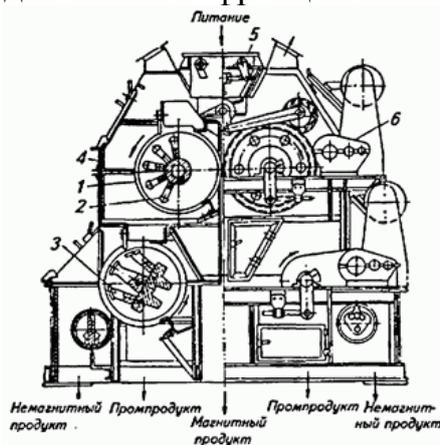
Магнитный барабанный сепаратор типа 4ПБС-63/200: 1 – барабаны; 2, 3 – пятиполюсные и трехполюсные магнитные системы; 4 – рама с кожухом; 5 – приемная коробка с распределителем питания; 6 – редукторы привода
